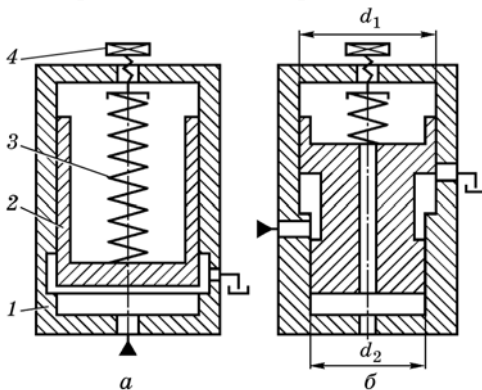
Переливні клапани прямої дії: *a* — золотниковий; *б* — золотниковий диференціальний; 1 — корпус; 2 — золотник; 3 — пружина; 4 — регулювальний гвинт
